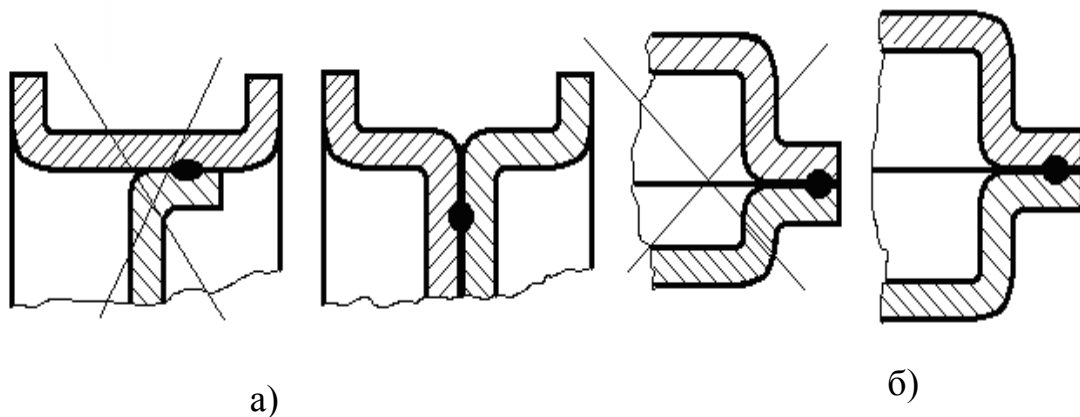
Уніфікація зварюваних деталей: а) зварний шків з двох різних деталей замінений на шків з двох однакових деталей; б) зварний бак з двох різних деталей замінений на бак з двох однакових деталей
